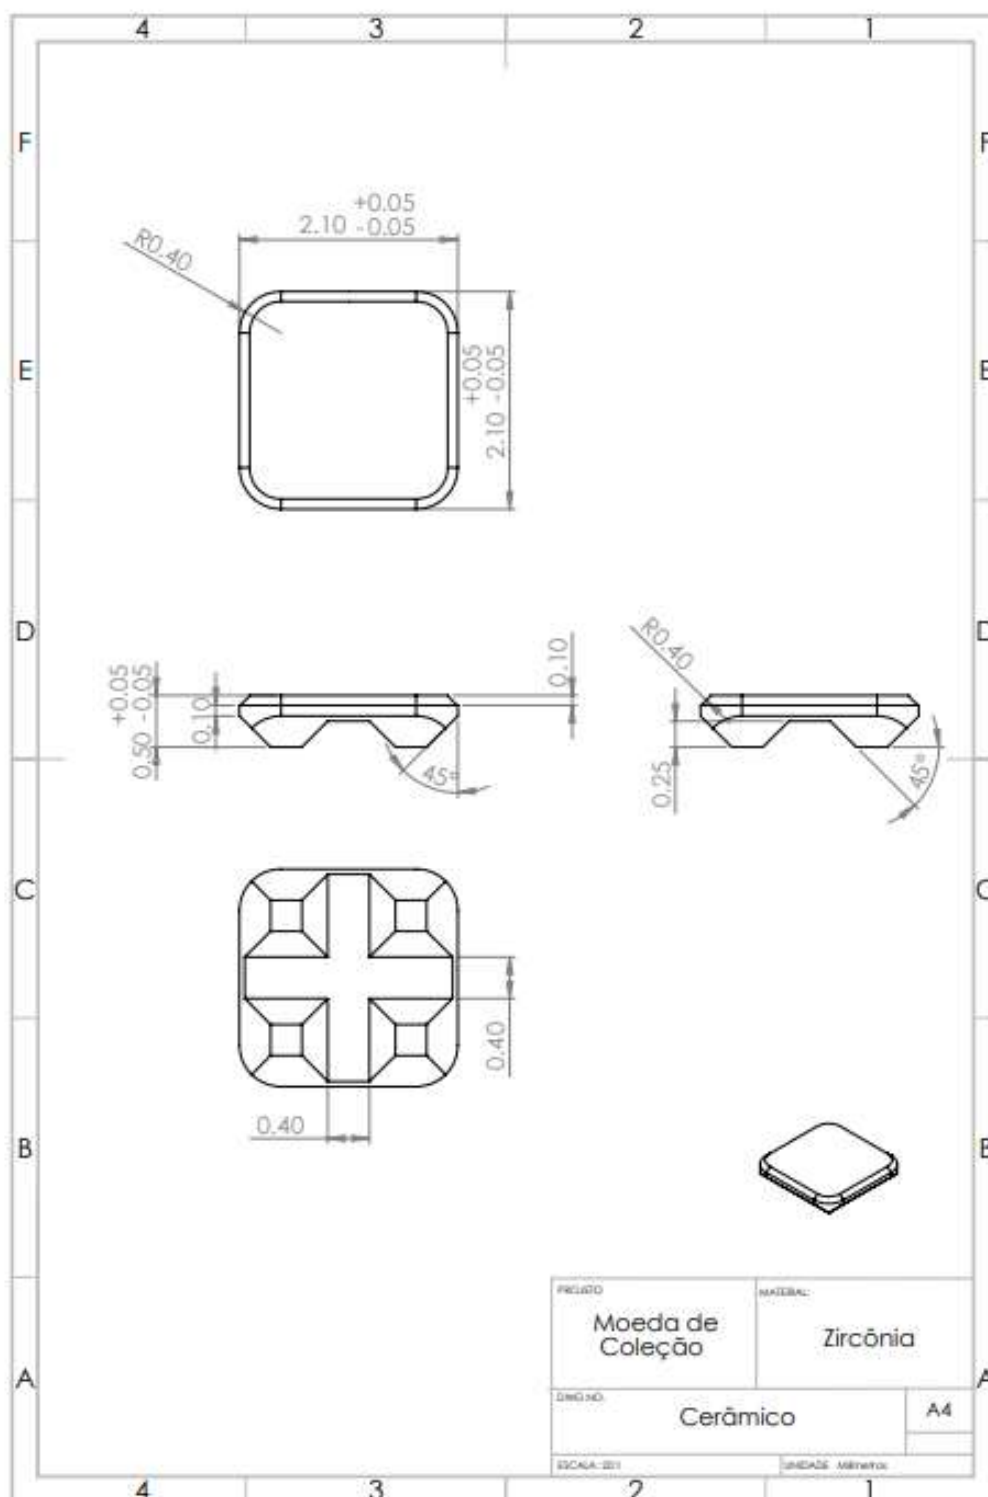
Desenho técnico com geometria, dimensões e tolerâncias (dimensões em milímetros).
